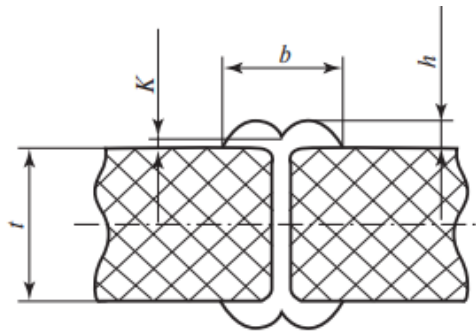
Основные геометрические размеры соединения встык труб из полиэтилена:  $t$  – толщина стенки трубы;  $b$  – ширина шва сварного соединения;  $h$  – высота шва сварного соединения;  $K$  – глубина впадины между валиками грата
